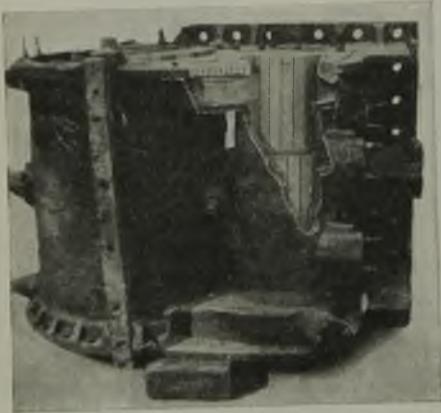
a. Lokomotivzylinder teilweise für die Schweißung vorbereitet.
